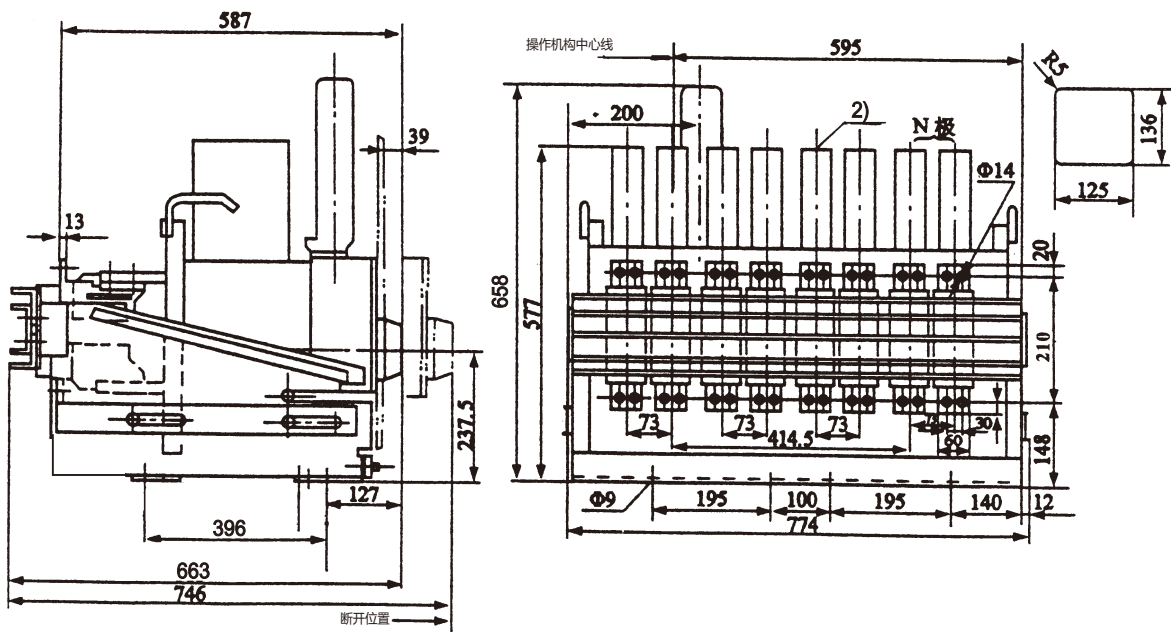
DW17D-2900/4(In=2900A)抽屉式断路器外形尺寸和安装尺寸
